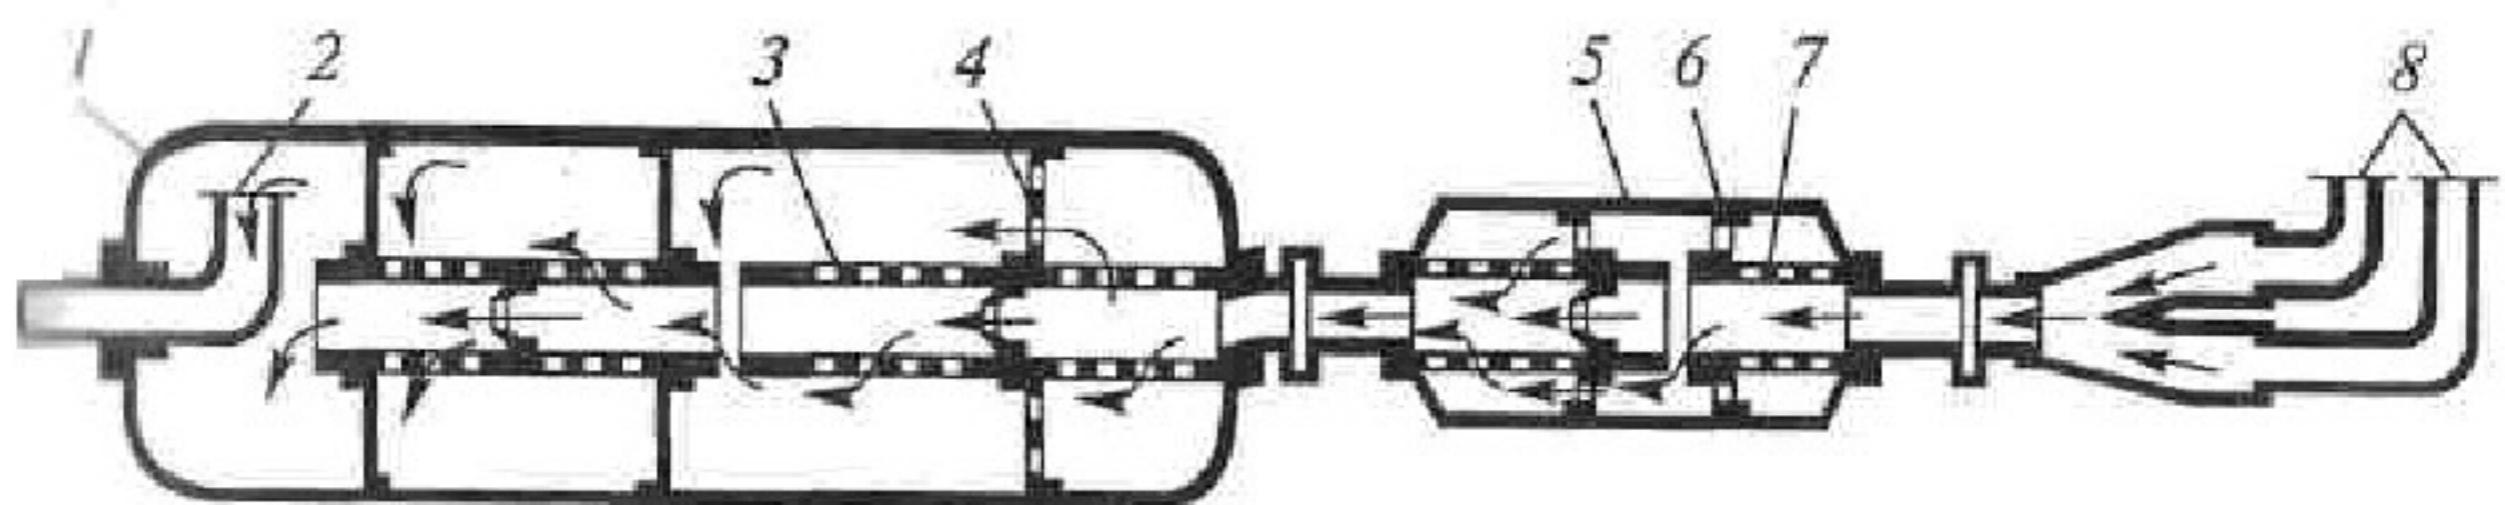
Глушители: 1 - основной глушитель; 2, 3, 7, 8 — трубы; 4, 6 — перегородки; 5 — дополнительный глушитель
